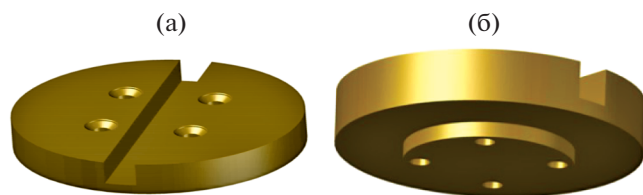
Внешний вид подложки для размещения образцов: а – вид сверху, б – вид снизу.
